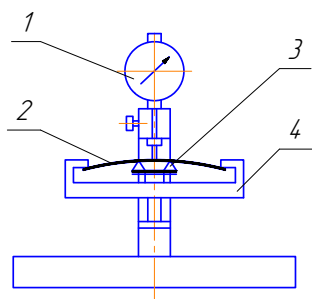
Нагружающее устройство: 1 – головка измерительная часового типа; 2 – образец; 3 – вкладыш; 4 – скоба
